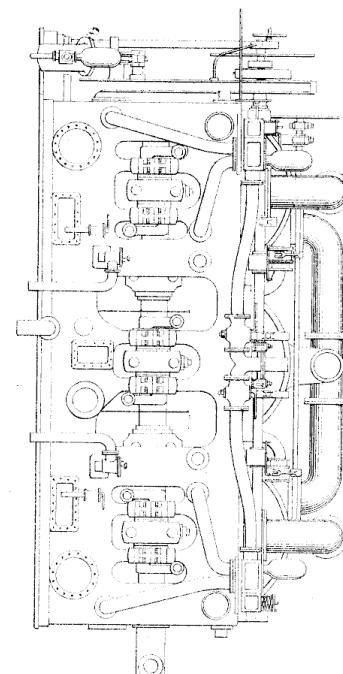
et 409. Machine horizontale à 2 cylindres.
